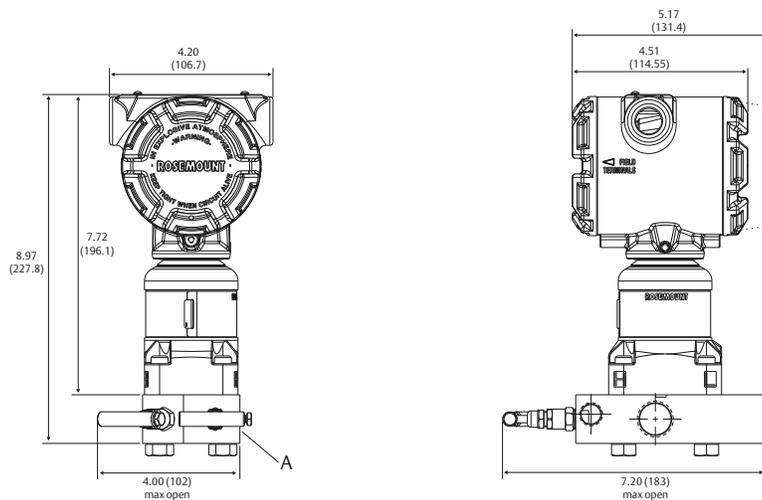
Копланарный клапанный блок модели 305 с пятью вентилями
